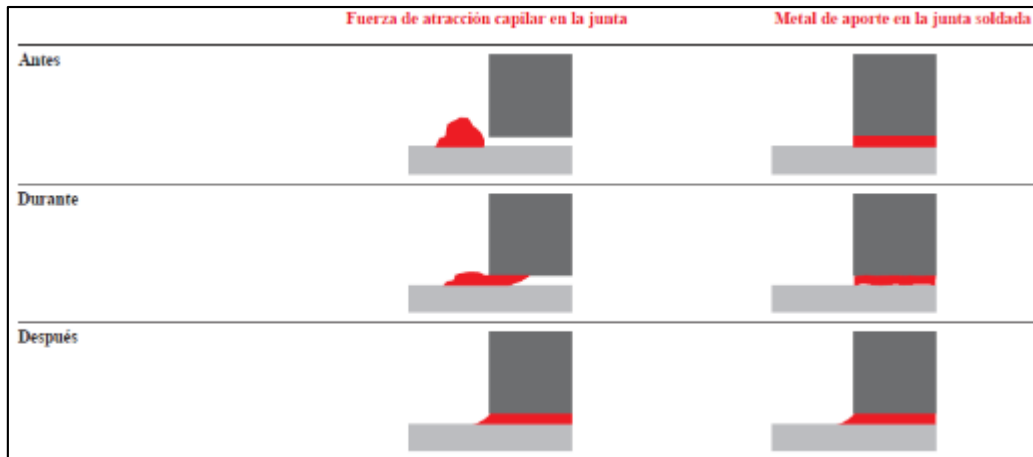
Efecto de la capilaridad en una junta soldada por soldadura indirecta.
